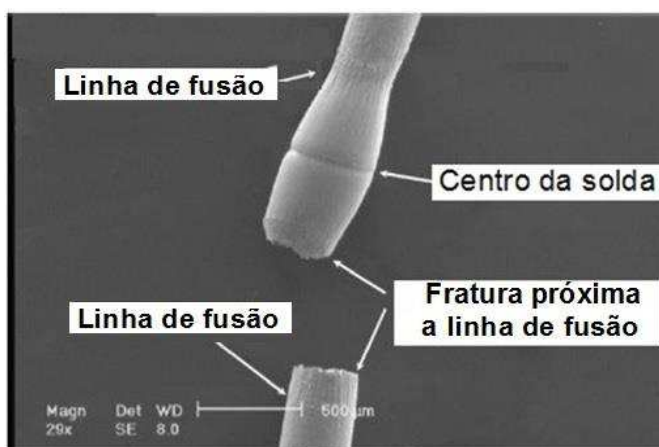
Região de fratura das juntas de Ni-Ti/Ni-Ti soldadas a laser (adaptado de Mirshekari *et al.*, 2013).
